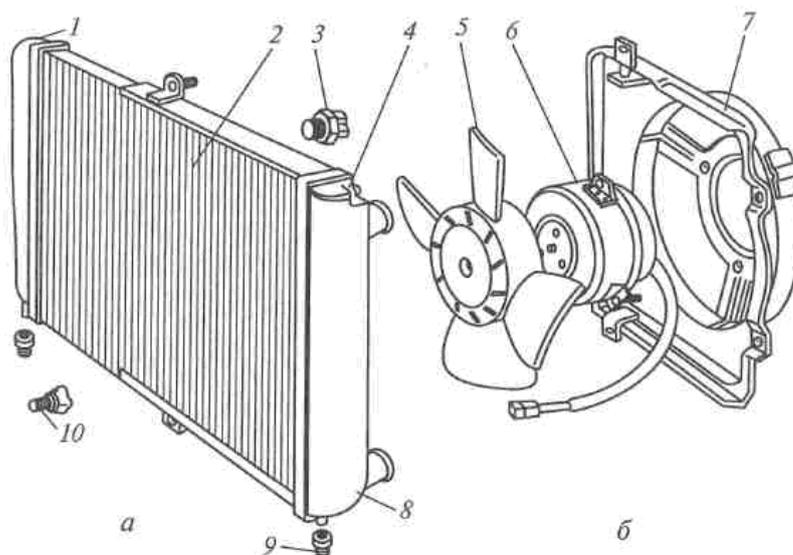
Разборный радиатор (а) и электровентилятор двигателя: 1,8 – бачки; 2 – сердцевина; 3 – датчик; 4 – прокладка; 5 – вентилятор; 6 – электродвигатель; 7 – кожух; 9 – опора; 10 – пробка.
